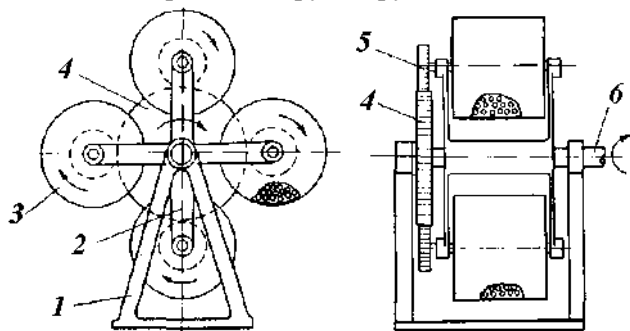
Схема планетарной мельницы: 1 – станина; 2 – водило; 3 – мельница; 4 – неподвижное зубчатое колесо; 5 – приводная шестерня; 6 – ведущий вал.
